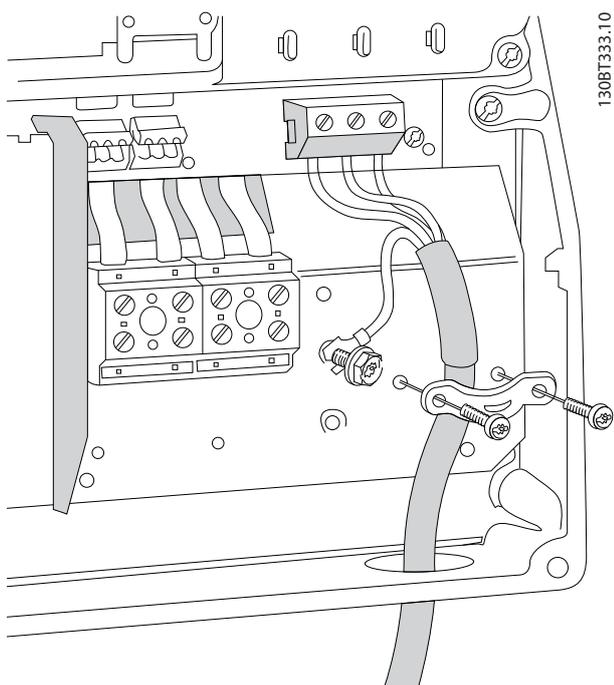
Raccordement du moteur pour protections de tailles B1 et B2
